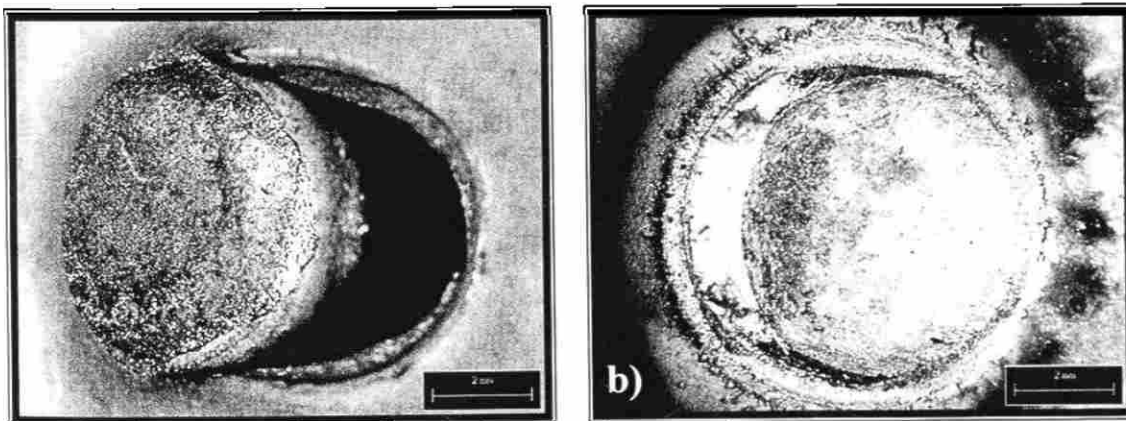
Botones de soldadura que presentan fractura regular después de haber sido ensayados. a) Ensayo de tensión con esfuerzo de corte. b) Ensayo de arranque.
